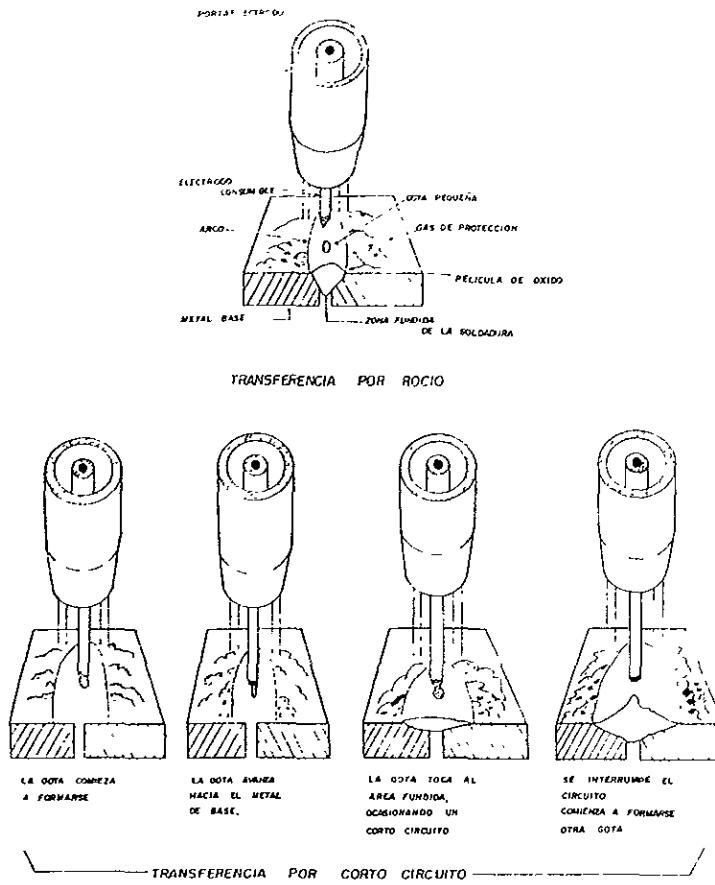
Soldadura de arco metálico y gas (GMAW).
